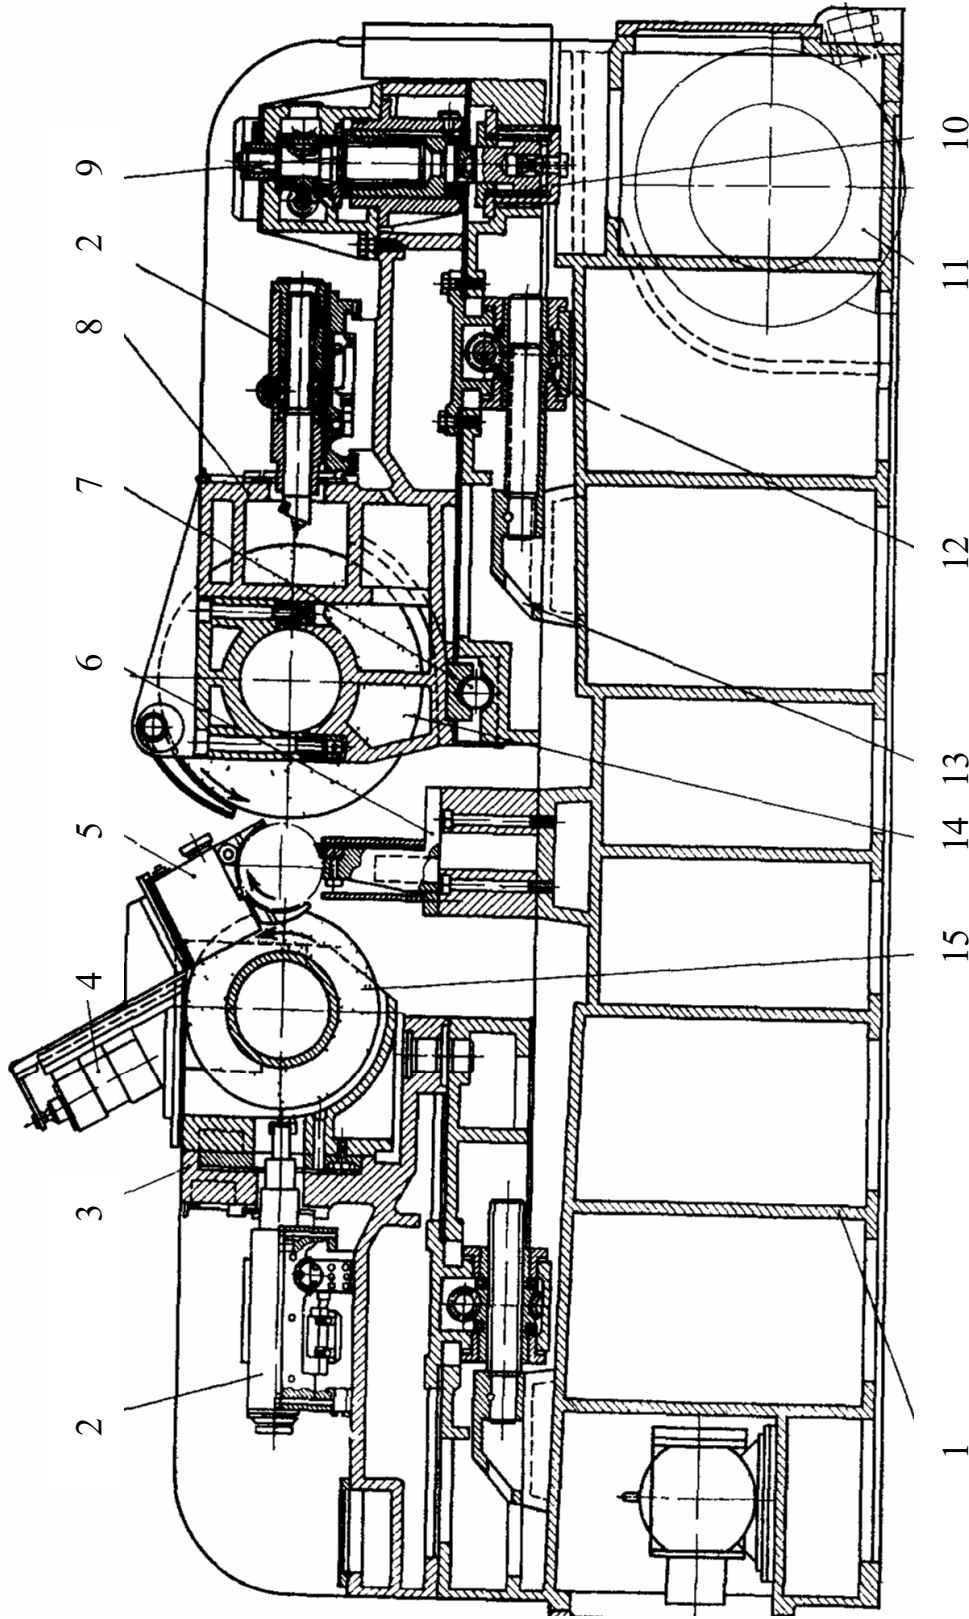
Безцентровий круглошліфувальний автомат: 1 – станина; 2 – механізм правки; 3 – бабка ведучого круга; 4 – гідроциліндр подачі вимірювального пристрою; 5 – вимірювальний пристрій; 6 – супорт; 7 – вісь повороту шліфувальної бабки; 8 – бабка шліфувального круга; 9 – домкрат і механізм подачі; 10 – циліндр швидкого підводу; 11 – привод шліфувального круга; 12 – механізм ручного переміщення полозків; 13 – полозки; 14, 15 – шліфувальний і ведучий круги
